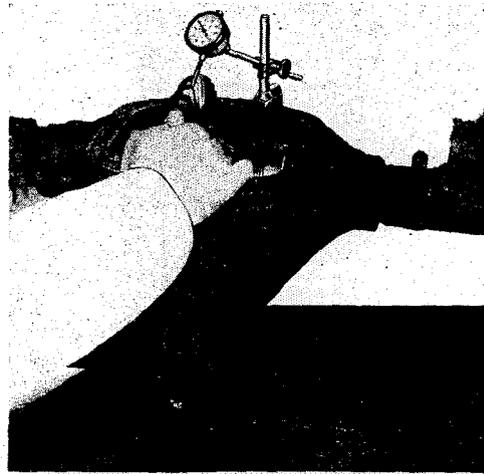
Uhr zum Prüfen des Zahnflankenspiels
